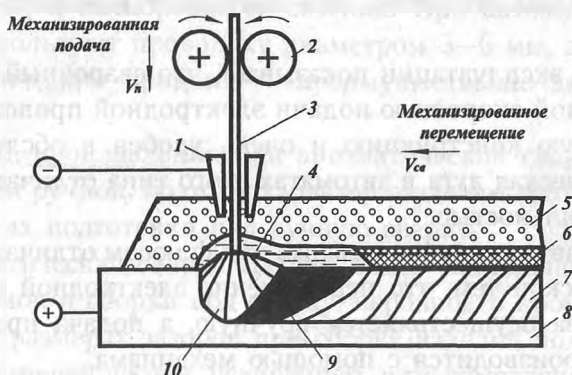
Схема автоматической дуговой сварки под флюсом: 1 — токопроводящая втулка; 2 — подающие ролики; 3 — сварочная проволока; 4 — жидкий шлак; 5 — флюс; 6 — застывший шлак; 7 — сварной шов; 8 — деталь; 9 — жидкий металл; 10 — электрическая дуга
